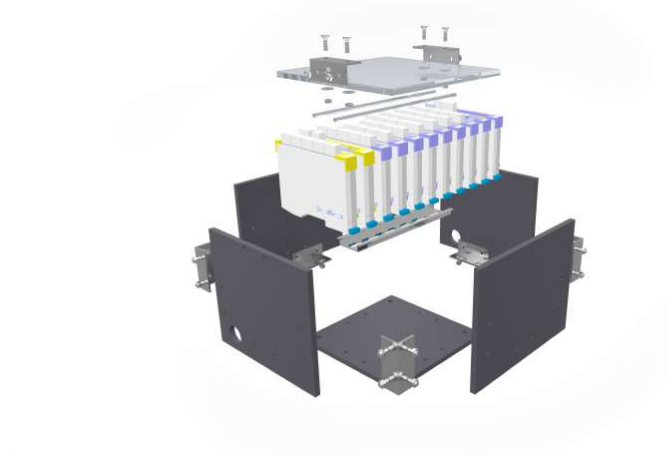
3D Ansicht der SPS-Explosionszeichnung
